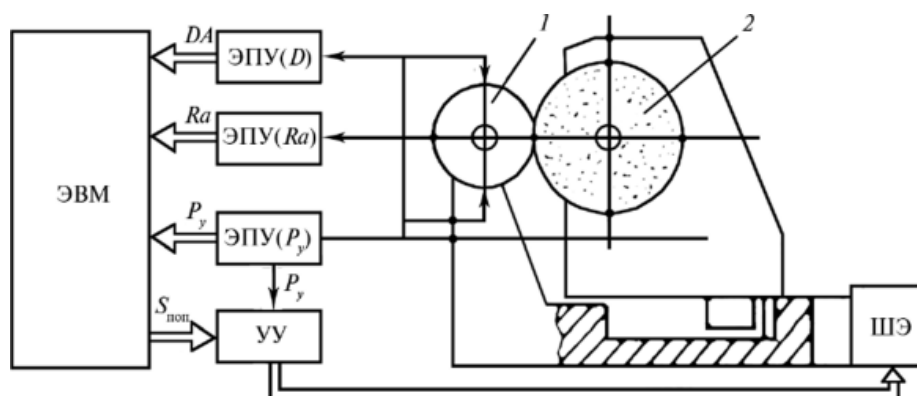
Система адаптивного управления процессом шлифования заготовки [92]:
